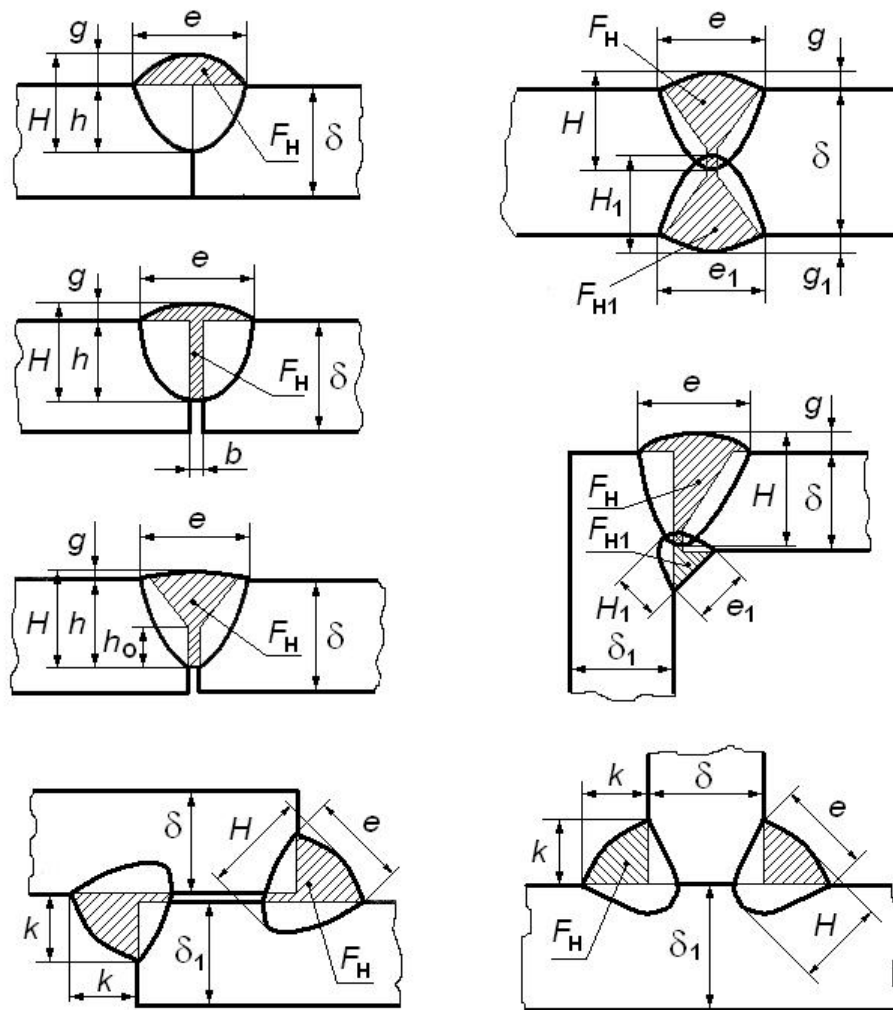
Исходные геометрические размеры сварных швов при расчете основных параметров режима сварки
